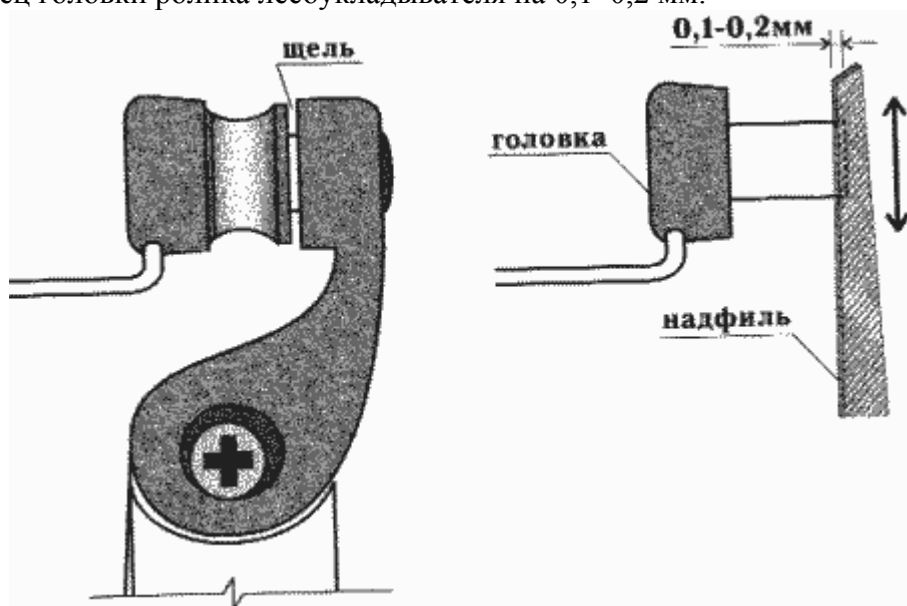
Щель между роликом и рычагом лесоукладывателя
